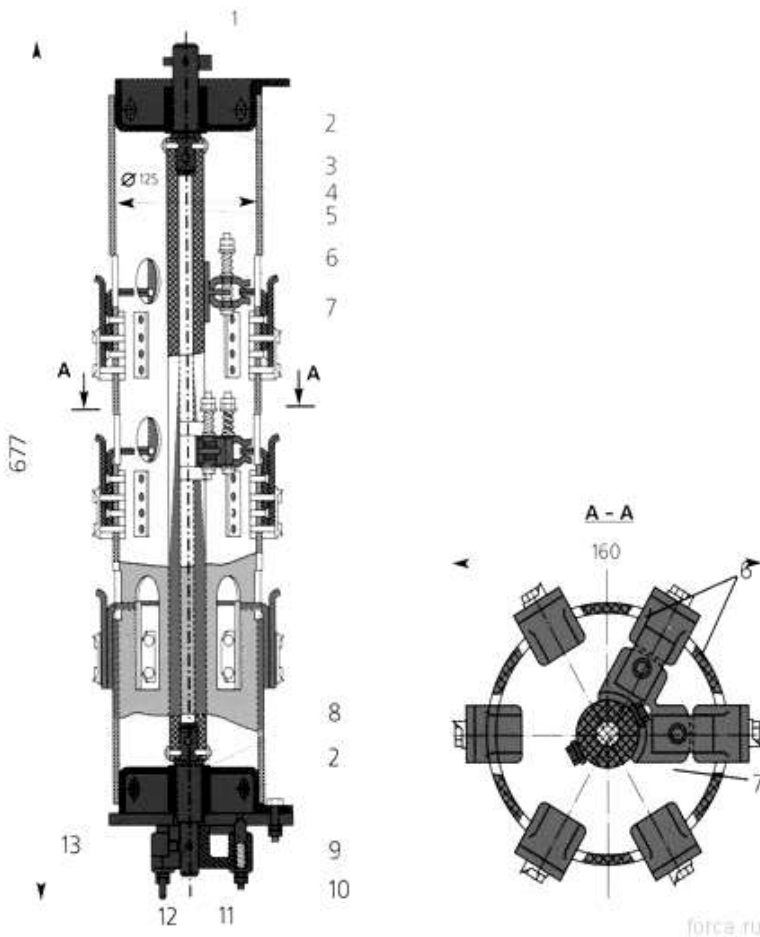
Трифазний перемикаючий пристрій ПТЛ-6-200/10: 1 - вал сталевий; 2 - фланець, 3 - втулка підшипника; 4 - корпус, 5 - бакелітова трубка; 6 - рухливі контакти; 7 - нерухомі контакти; 8 - вал сталевий; 9 - болт кріпильний; 10 - фіксатор положення; 11 - палець фіксатора; 12 - кріпильний штифт фіксатора; 13 - диск з фіксуєчими отворами.
